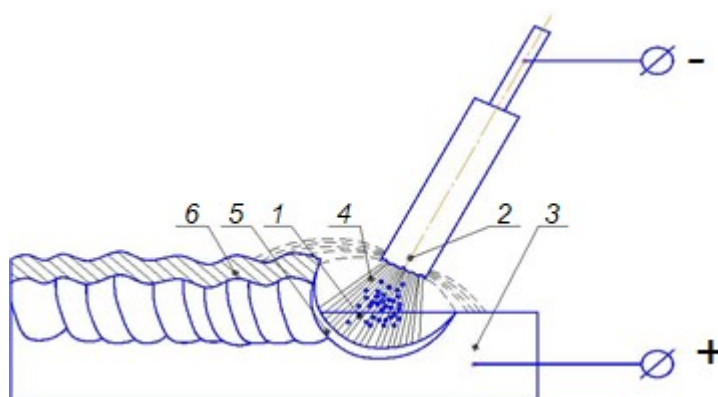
Ручная дуговая сварка покрытым электродом
